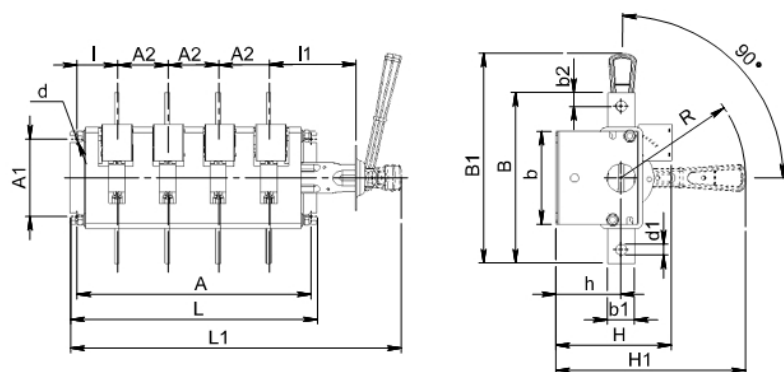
Б Выключатель-разъединитель на одно направление 4-полюсный с боковой смещенной рукояткой
